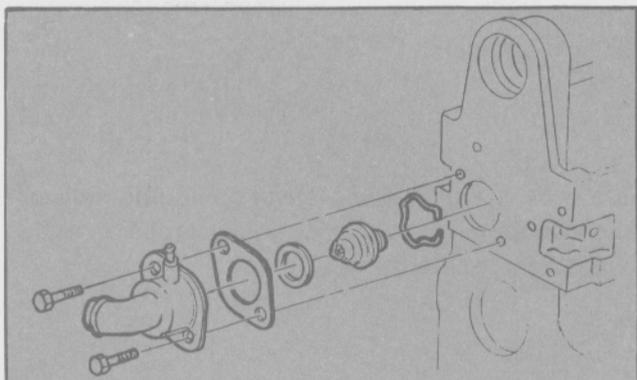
Desmontaje del termostato (Motor I4-1,6L).
